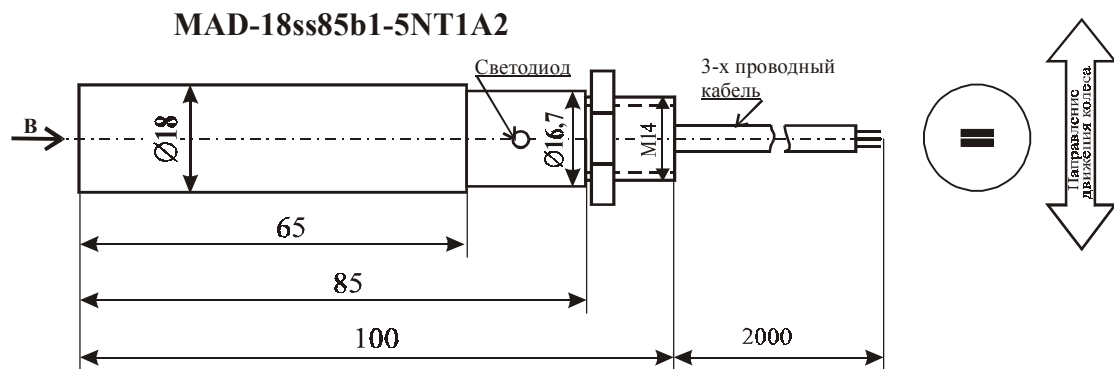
Внешний вид и габаритные размеры датчиков типа MAD-18ss85b1-5NT1A2
